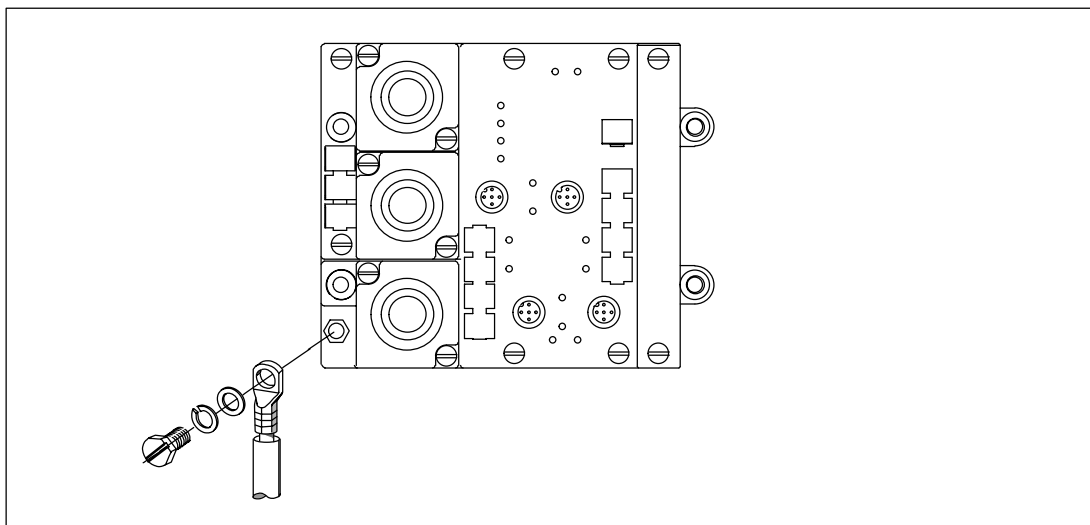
Collegamento del modulo base BM 141, 142 e 147/CPU alla terra di protezione
